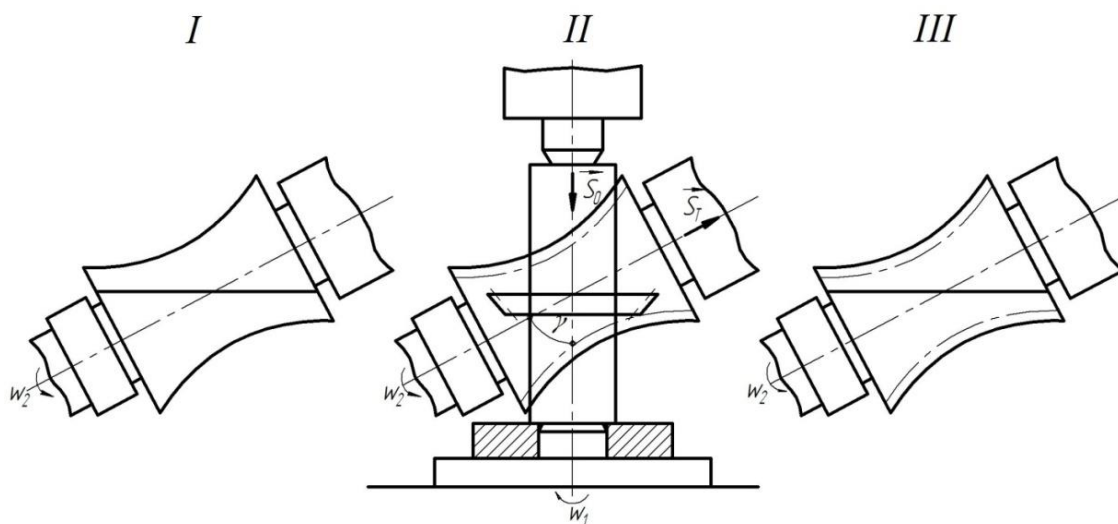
Схема изготовления гиперболических зубчатых колес
